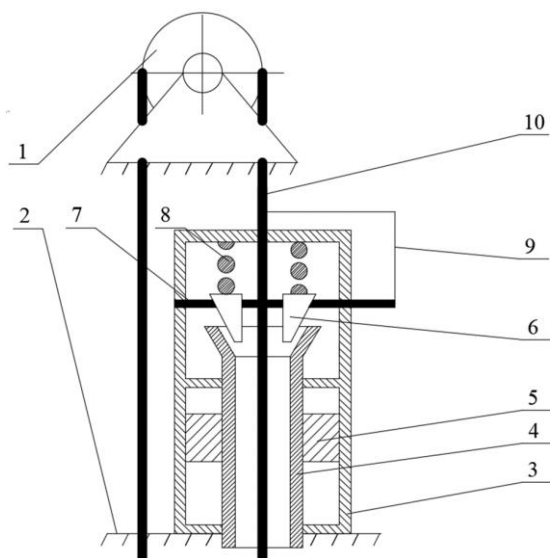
Уловлювач для вантажопідйомних машин: 1 – зрівняльний блок; 2 – металоконструкції зрівняльного блоку; 3 – пневматичний гальмівний циліндр; 4 – шток; 5 – поршень; 6 – гальмові елементи; 7 – стопор; 8 – пружина; 9 – механічний датчик швидкості канату; 10 – гілка вантажного канату
